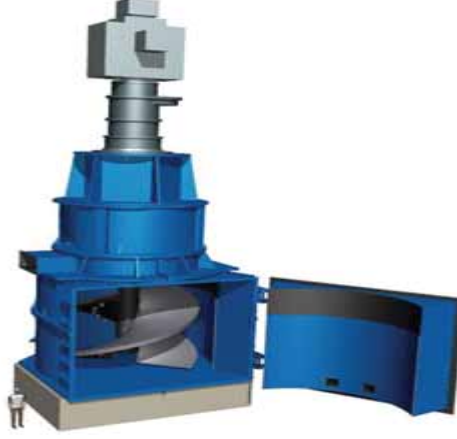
MaxxMill değirmeni genel tasarımı
